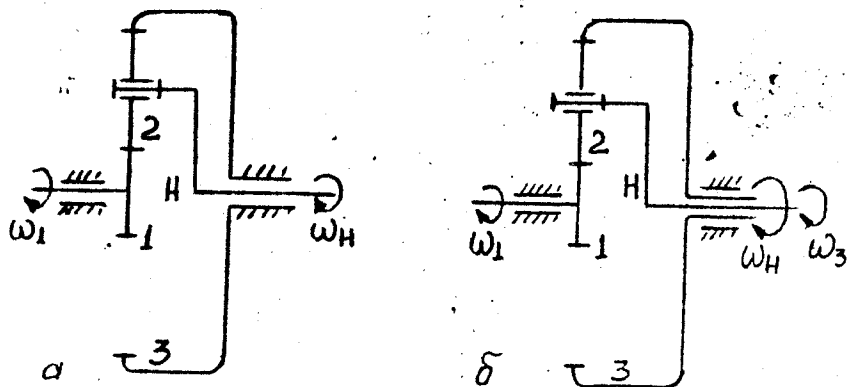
Планетарні механізми: а - редуктор; б - диференціал
